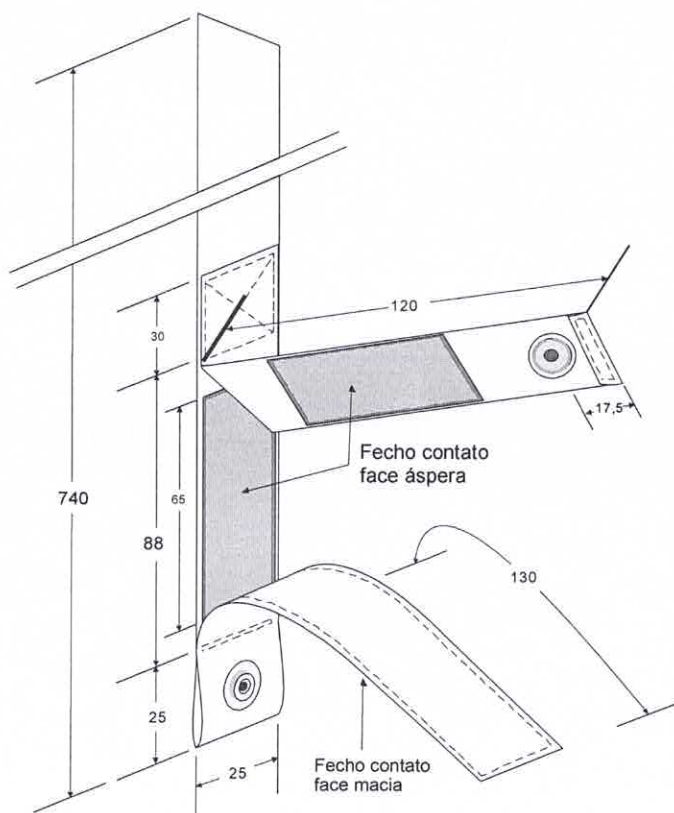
VISTA DO TIRANTE DIANTEIRO (MEDIDAS EM MM)
